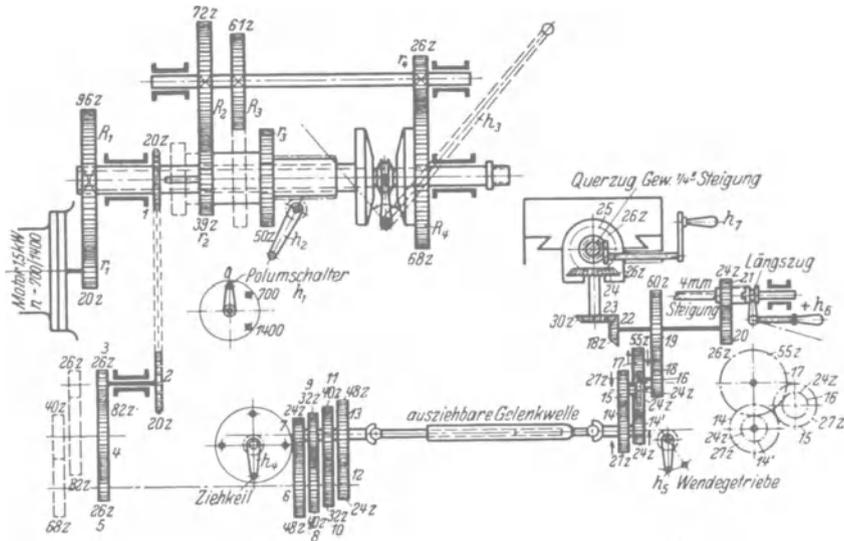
Getriebeplan einer allgemeinen Fräsmaschine.
